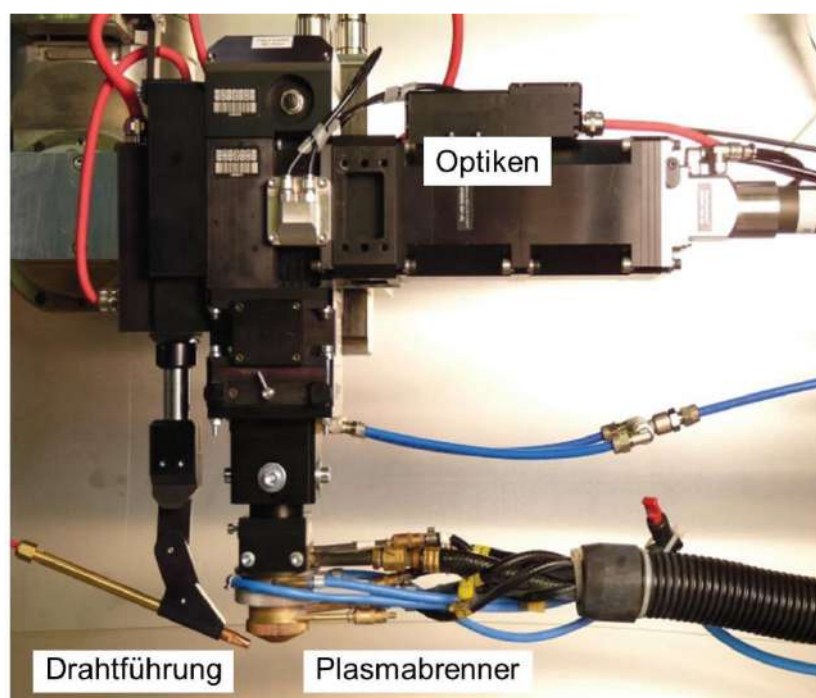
Інтегрована головка для лазерно-плазмового зварювання із системою подачі присаджувального дроту [90].
